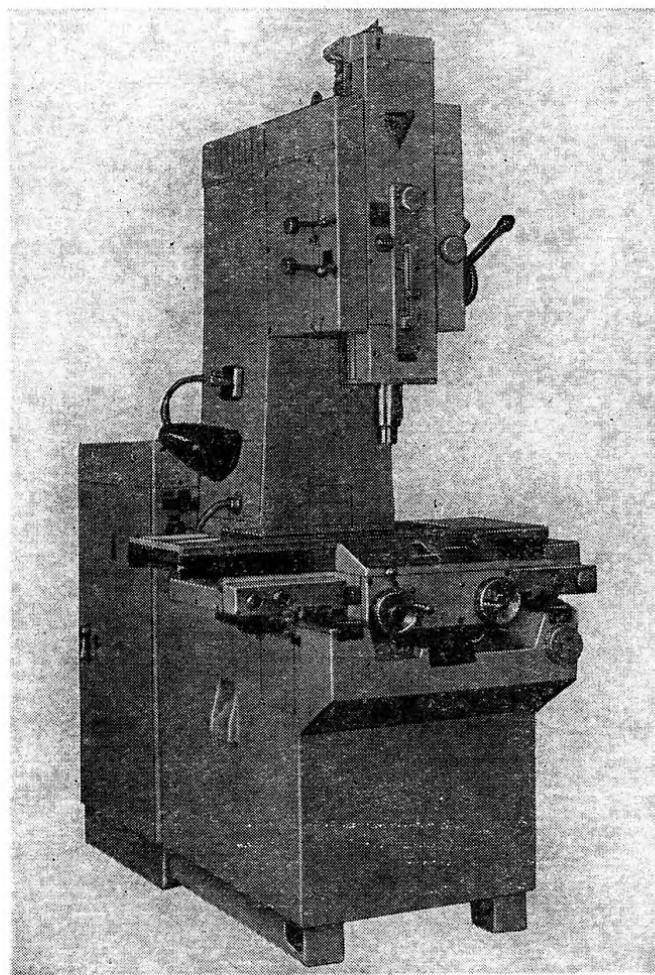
Общий вид координатно-расточного одностоечного станка 2421
